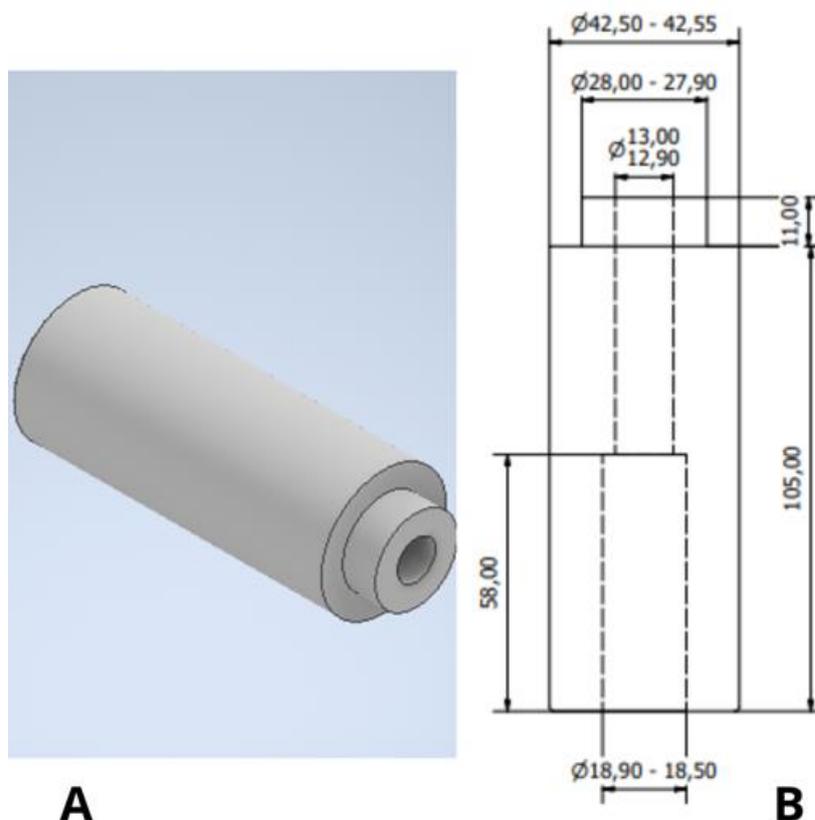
(A) Desenho 3D do eixo guia; (B) desenho 2D do eixo guia.
